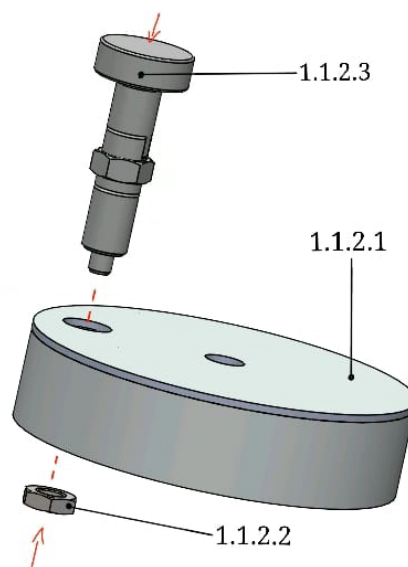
Análisis de montaje 1.1.2
